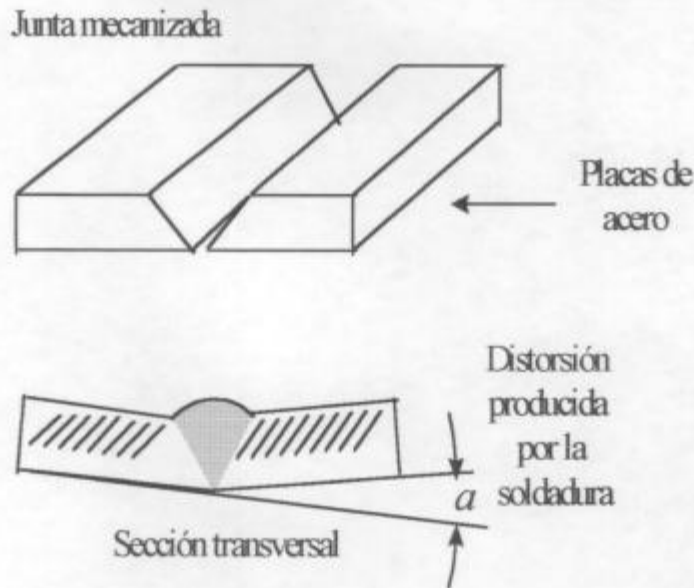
Distorsión geométrica producida por la soldadura de arco eléctrico
